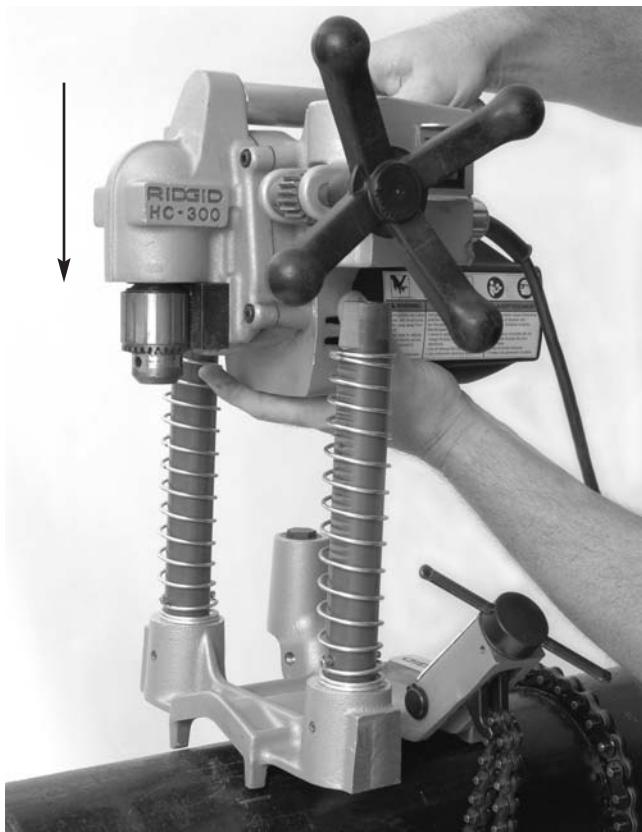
Montaje del motor de la HC-300 a la base de la máquina
